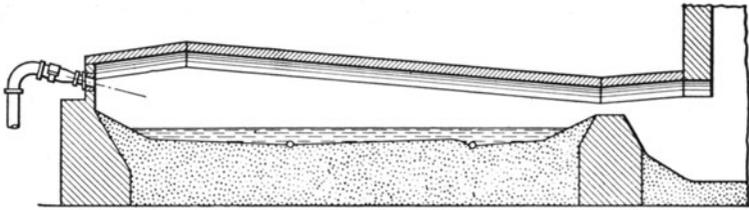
¹⁾. Flammofen neuerer Bauart mit 2 Stichlöchern. (Grindley Fuel Equipment Co.)
